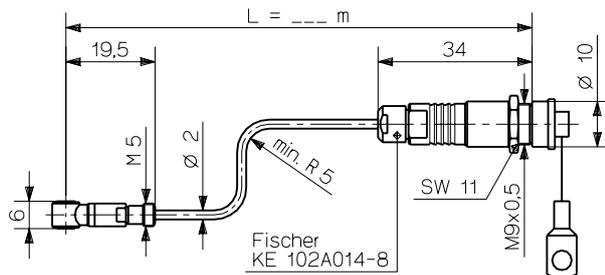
Kraftsensor Typ 9211B... mit Kabel und Stecker Standardlängen: 0,2 ... 3,0 m (siehe Bestellschlüssel)
